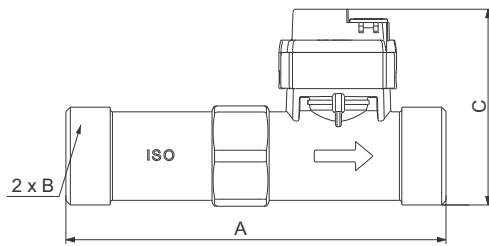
Abmessungen des Sensors VFS QT 5-100 l/min (mit Gewinde)
